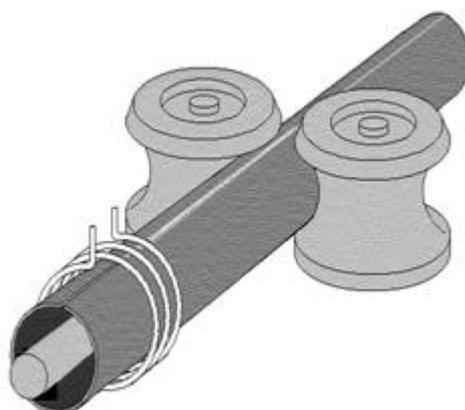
Ilustração do Processo de Soldagem por Alta Frequência. Fonte InoxTubos.
